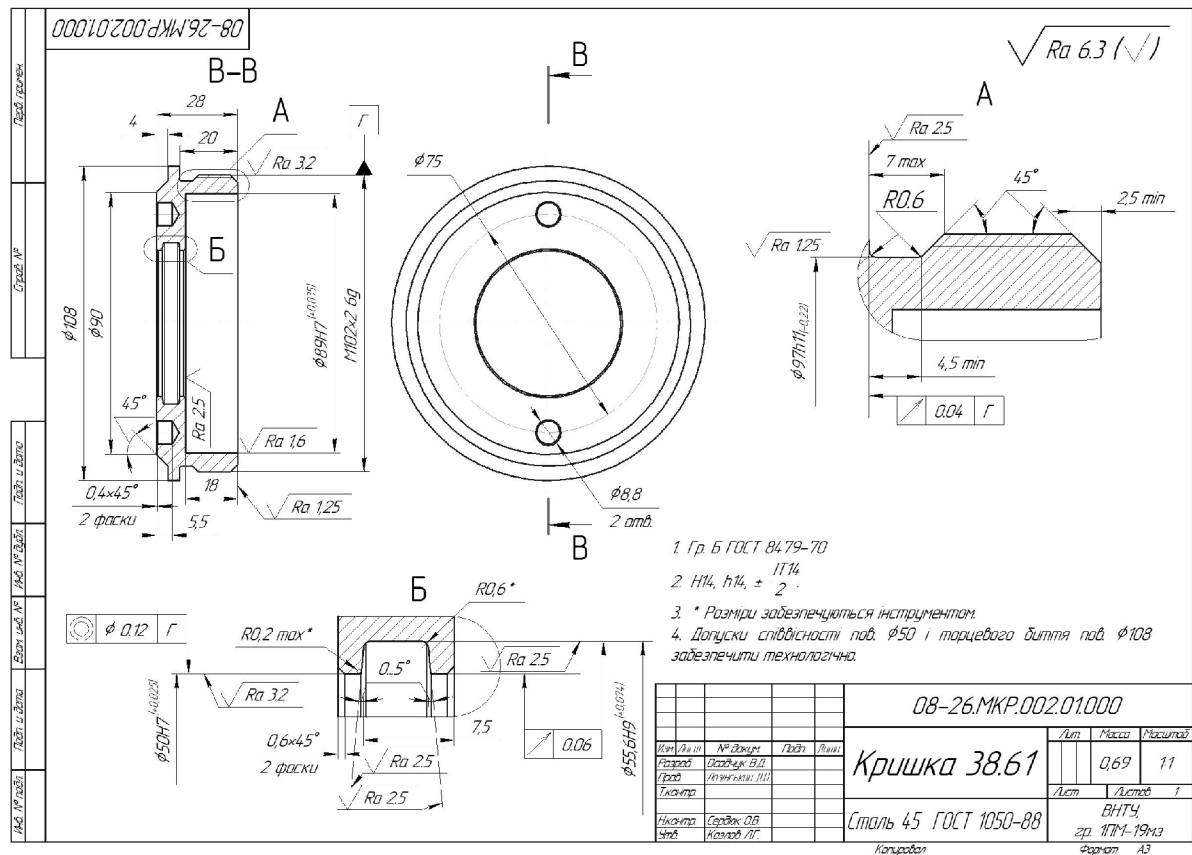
Креслення деталі «Корпус 38.61»
